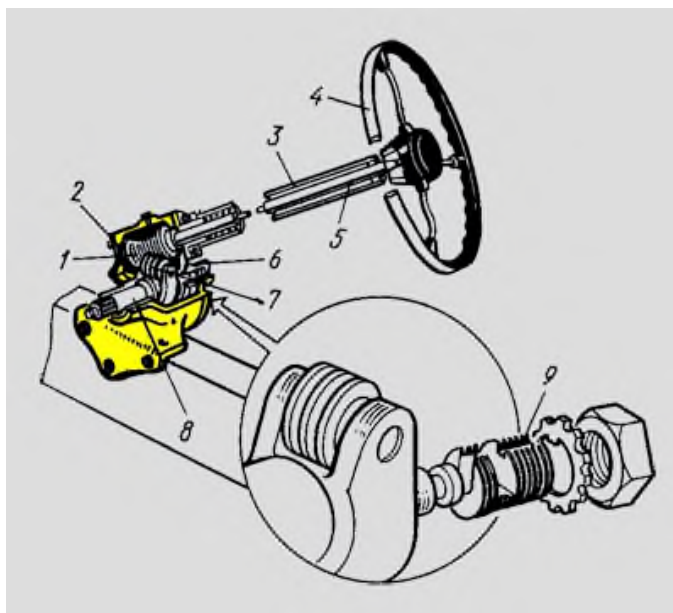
Рулевой механизм автомобиля ГАЗ-53А
